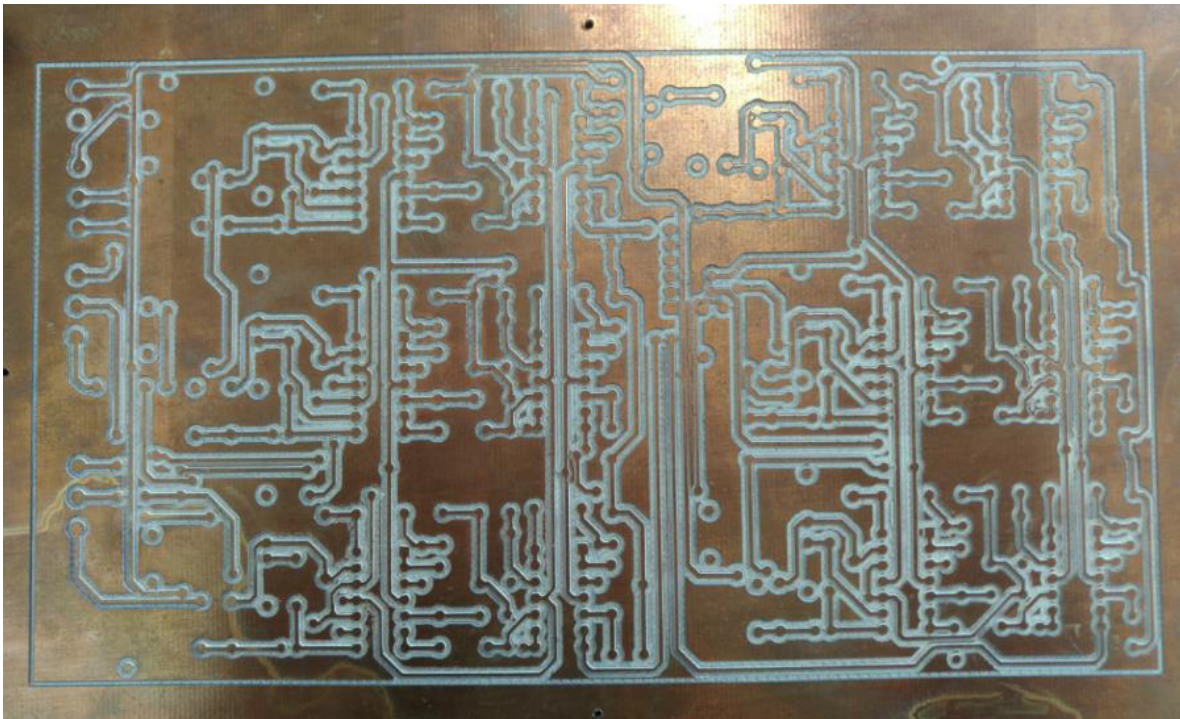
PCB impreso para obtener 6 señales del plano horizontal del ECG.
